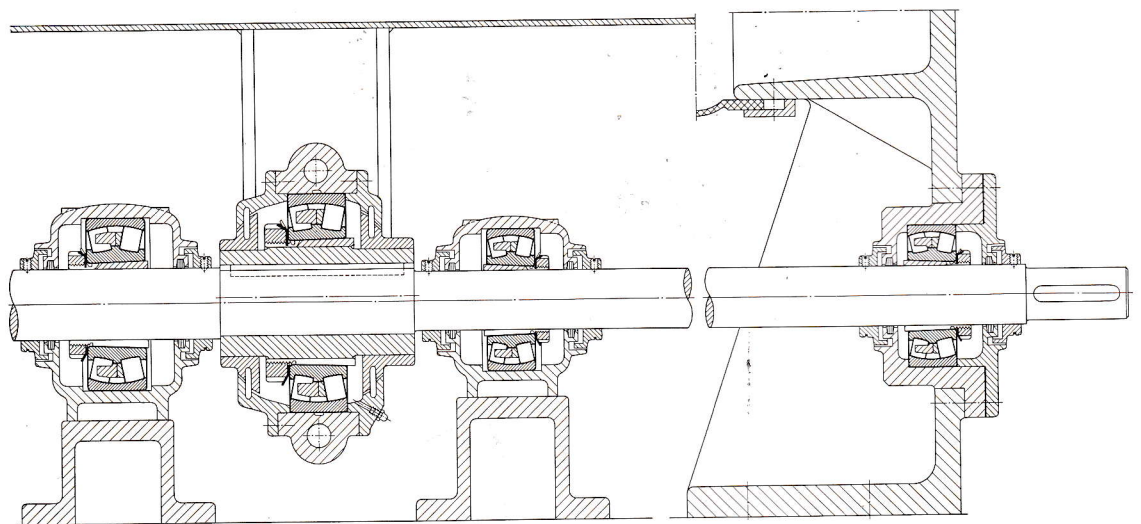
Disposición de rodamientos del eje excéntrico del colador según la fig. 9
